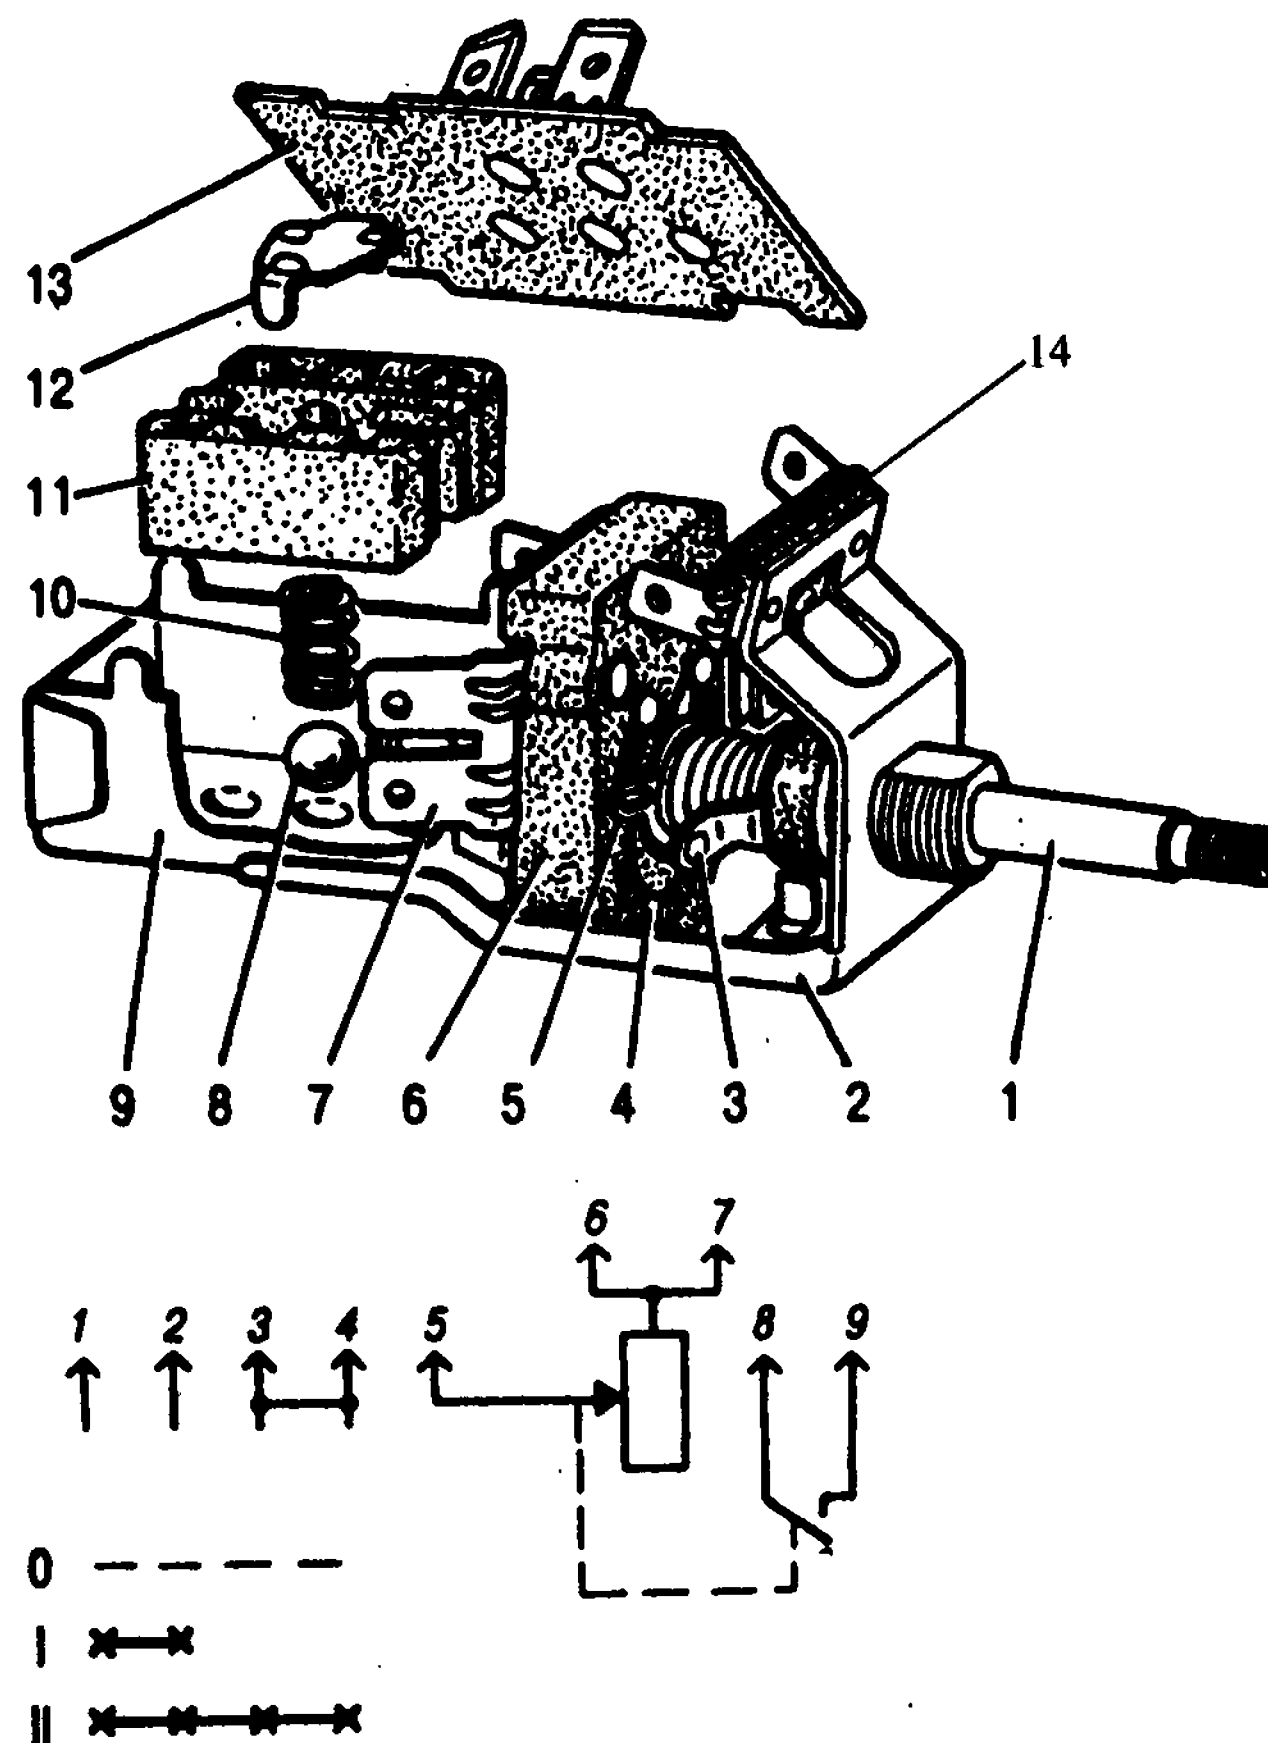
Центральный переключатель света и его схема: 1 - шток, 2 - кронштейн, 3 - контакт включения плафона, 4 - резистор, 5 - подвижный контакт резистора, 6 - изолятор резистора, 7 - штекер, 8 - шарик, 9 - корпус, 10 - пружина, 11 - каретка, 12 - подвижный контакт каретки, 13 - панель с контактами, 14 - выключатель плафона
